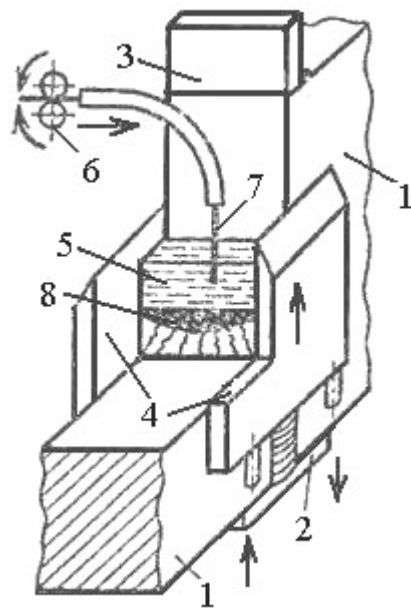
Схема электрошлаковой сварки: 1 – заготовки; 2, 3 – специальные планки; 4 – ползуны; 5 – электропроводный шлак; 6 – механизм подачи; 7 – электродная проволока; 8 – сварочная ванна
